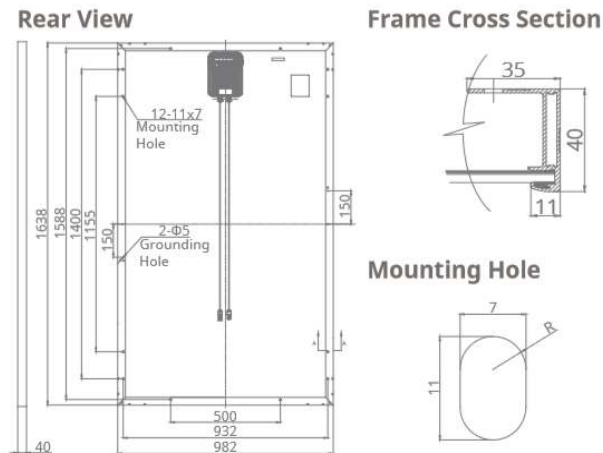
Dimensões da placa solar Canadian Solar CS6P-260P-SD, [18].
